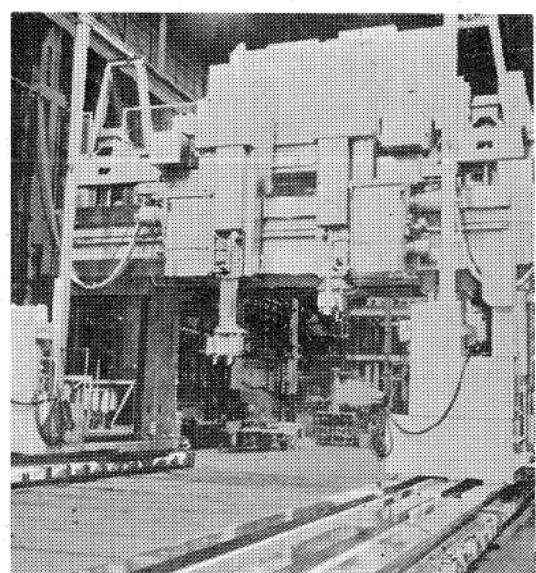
MORTON : DOUBLE BRIDGE GANTRY TYPE MACHINING CENTER, 2本のベッドの間に定盤上に加工物がおかれるが、写真に見えない手前にもう1本のBRIDGEがある：GE, West Lynn Mass. Medium Steam Turbine and Gear Dept. にて稼動中
